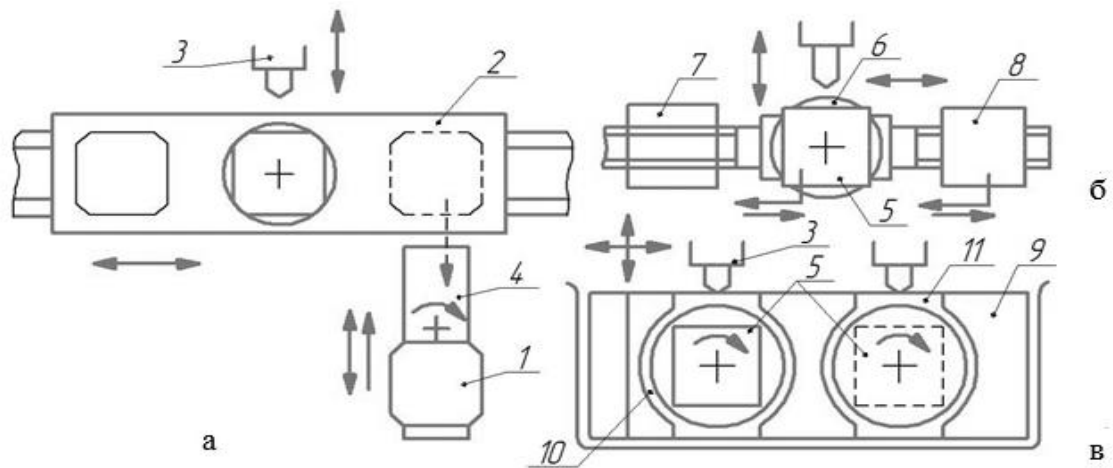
Способи кантування та заміни оброблюваних заготовок на верстатах з ЧПК
